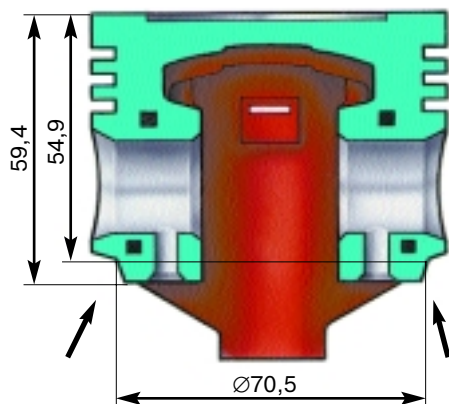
Схема удаления металла с поршня двигателя мод. 2106-70 для подгонки массы поршня (стрелками указаны места, на которых можно удалять металл)
